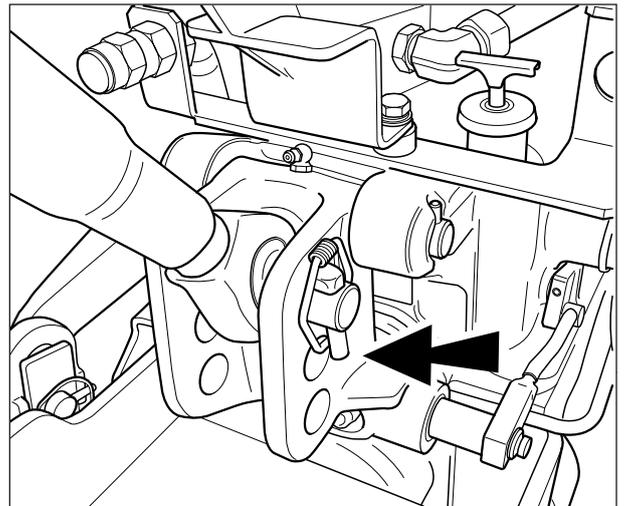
Dreipunktaufhängung für Kraftheber mit drei Anschlussbohrungen des Geräts
